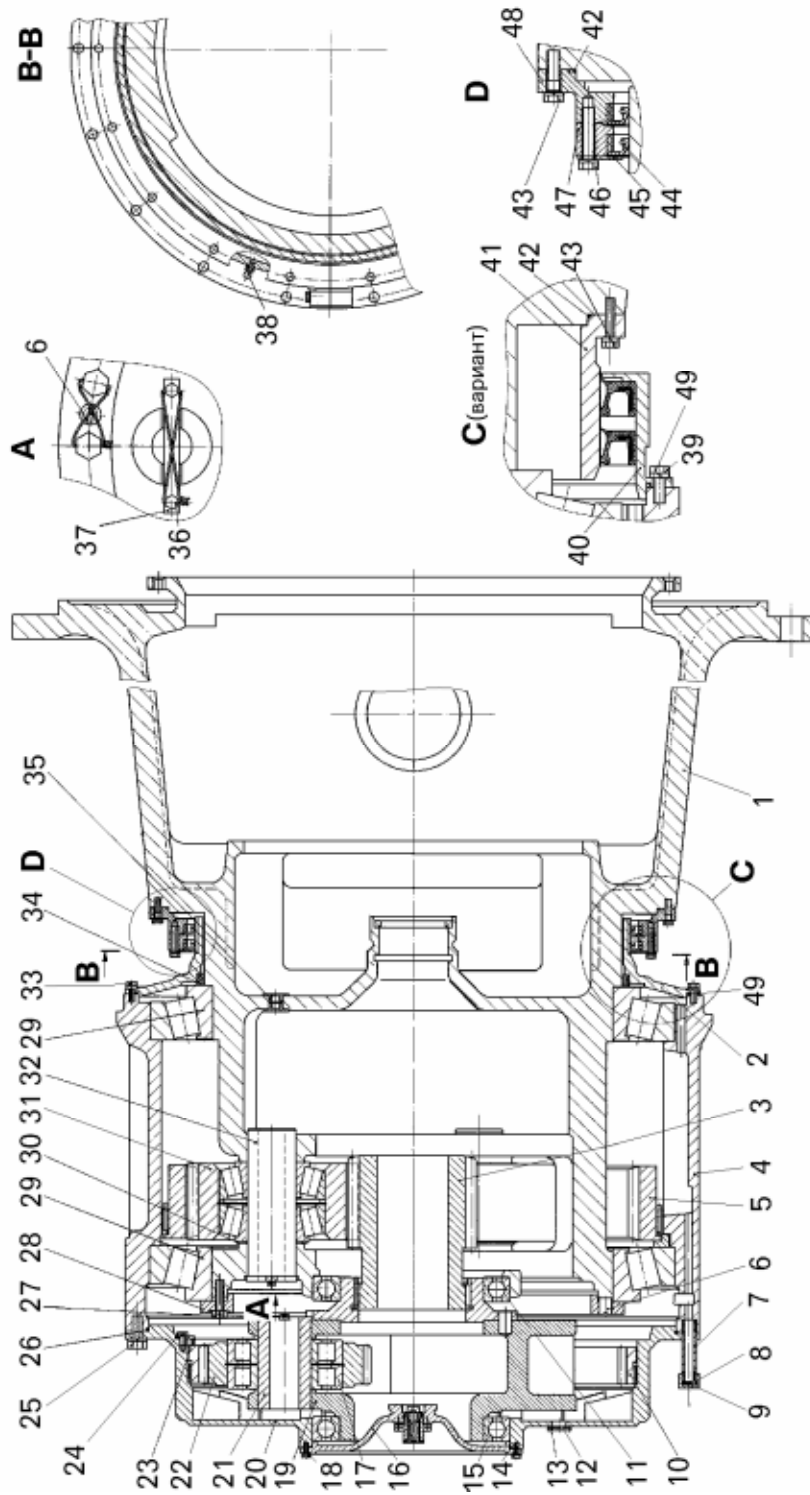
Редуктор мотор-колеса 7516:
